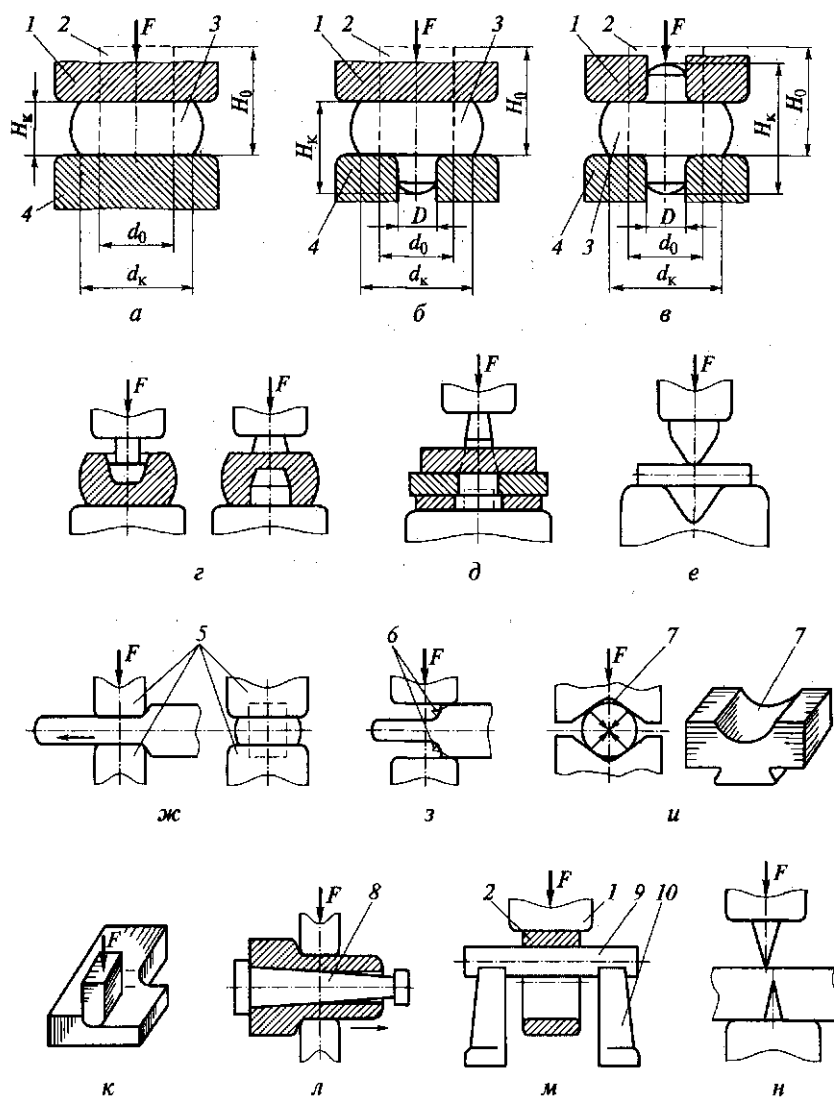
Схемы основных операций свободнойковки части заготовки:
